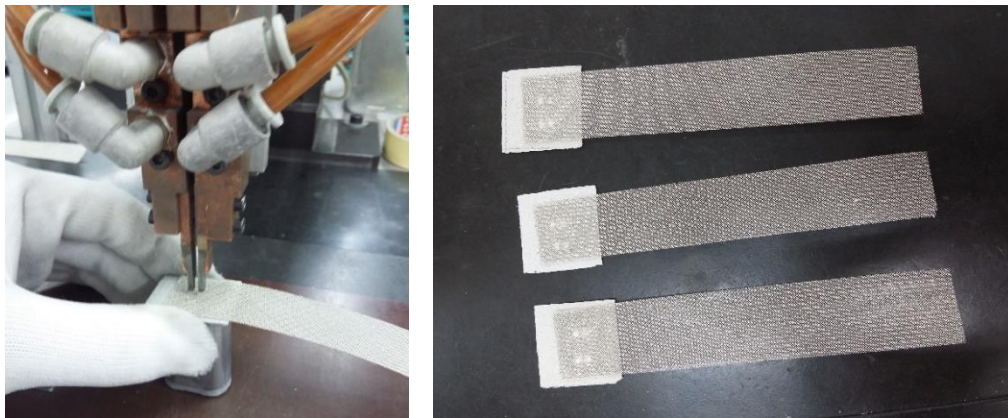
Execução do Processo de Soldadura por Pontos (à Esquerda) e Provetes Obtidos (à Direita).
